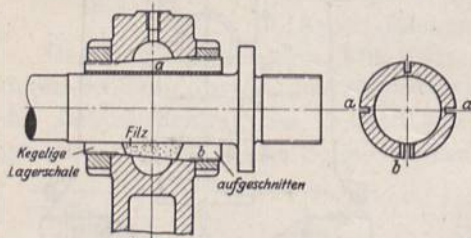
Nachstellbares Lager an Werkzeugmaschinen.
